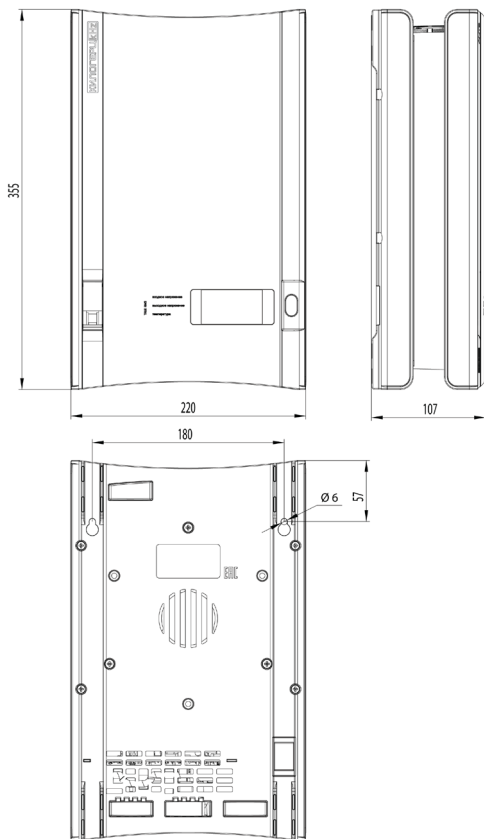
Габаритные и установочные размеры стабилизаторов КилоГерц У 1/16
